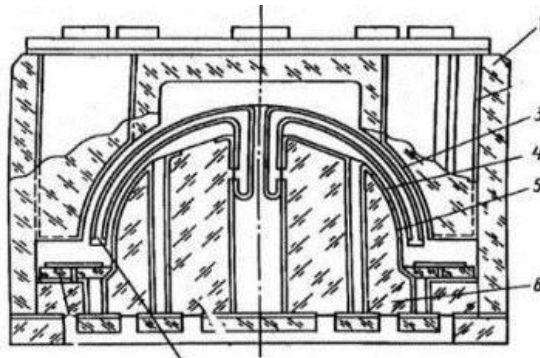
Конструкція корпусу із внутрішній ніжкою
